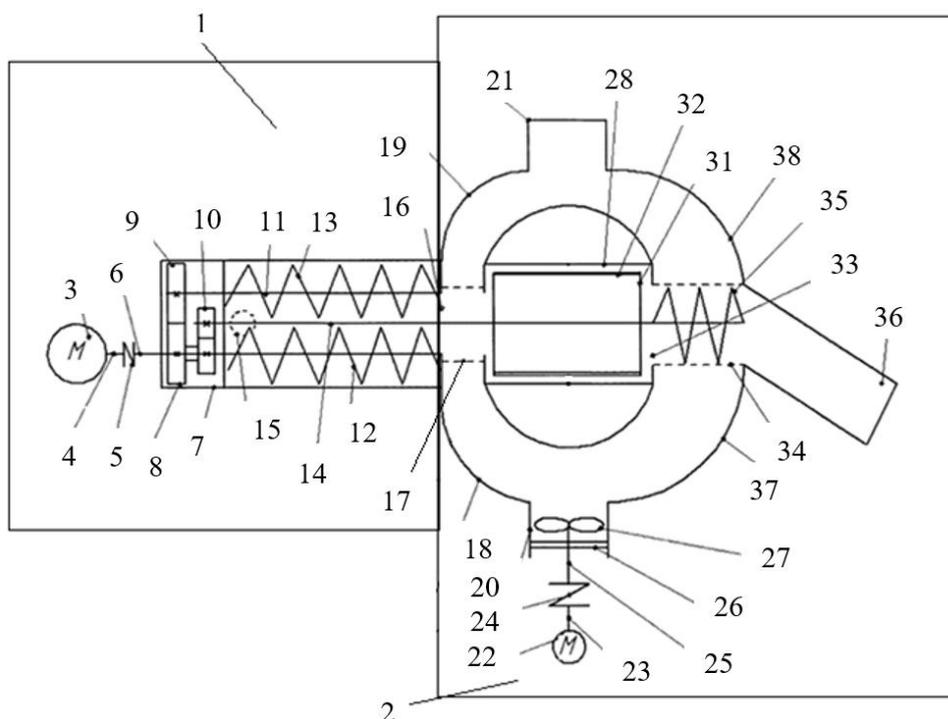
Кинематическая схема новой конструкции шелушителя
